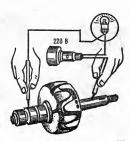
Проверка обмотки возбуждения замыкание с корпусом.
